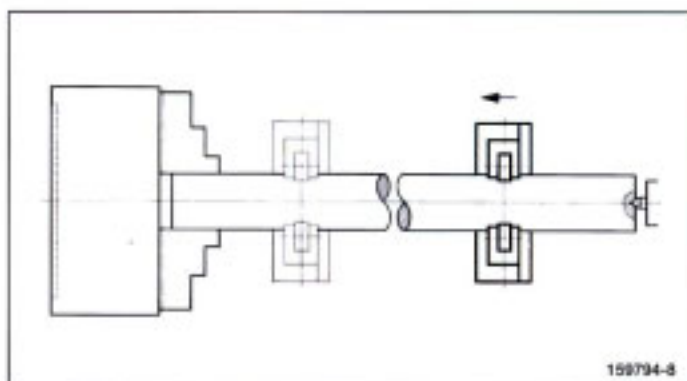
Mitlaufende Ausführung bei Bearbeitung z.B. langer Wellen
